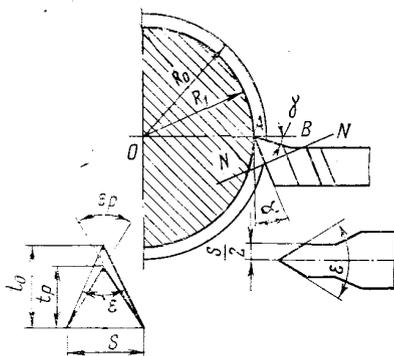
Схема коррекции профиля стержневого резьбового резца
